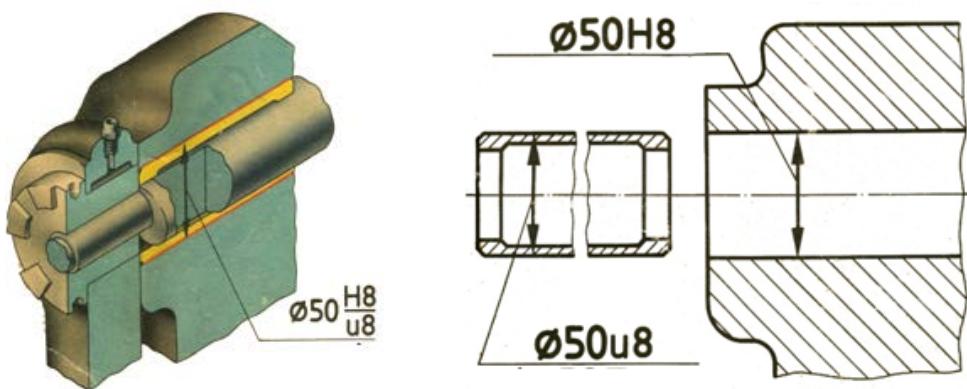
Втулка вала в станине эксцентрикового пресса
